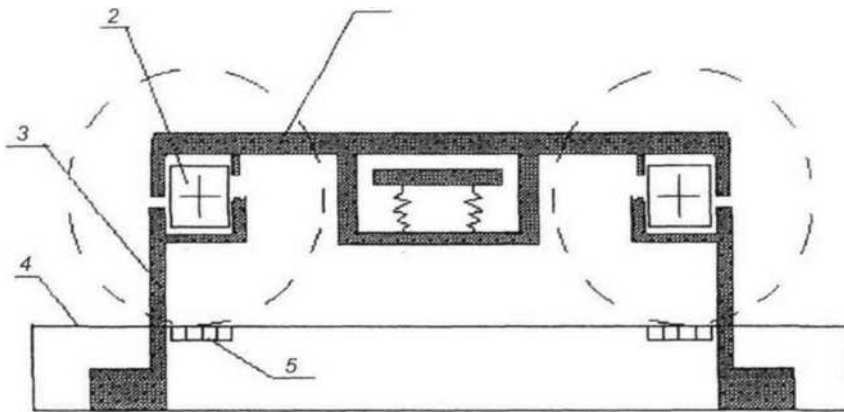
Стенд для перевірки монтажу візка моделі 18-100
